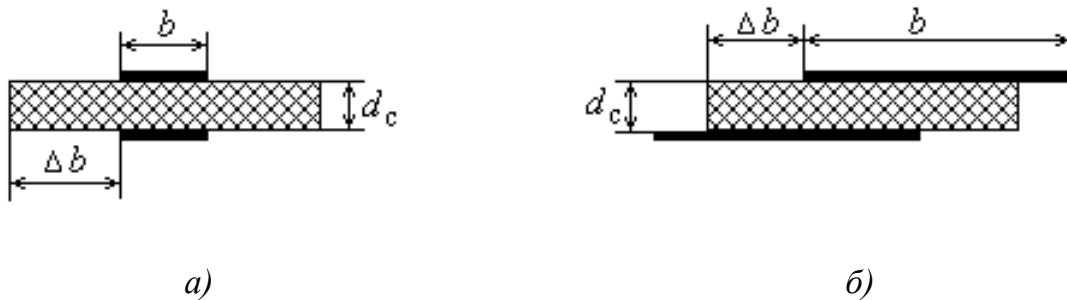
Способы намотки конденсаторных секций: а – для конструкции со скрытой фольгой, б – для конструкции с выступающей фольгой
